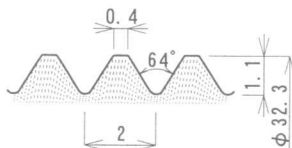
中空P C鋼棒ねじ部詳細図 (mm)
